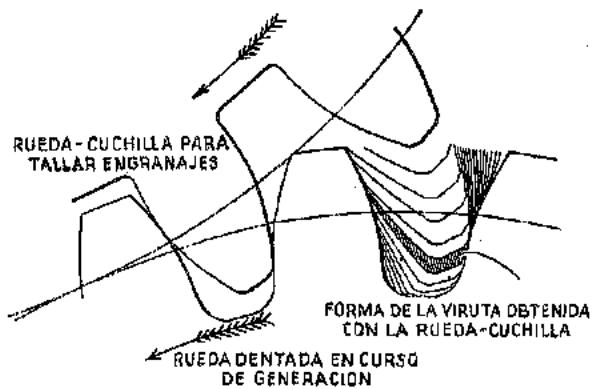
Acción de corte de un piñón mortajador de engranajes (Fellows Gear Shaper Co.)
